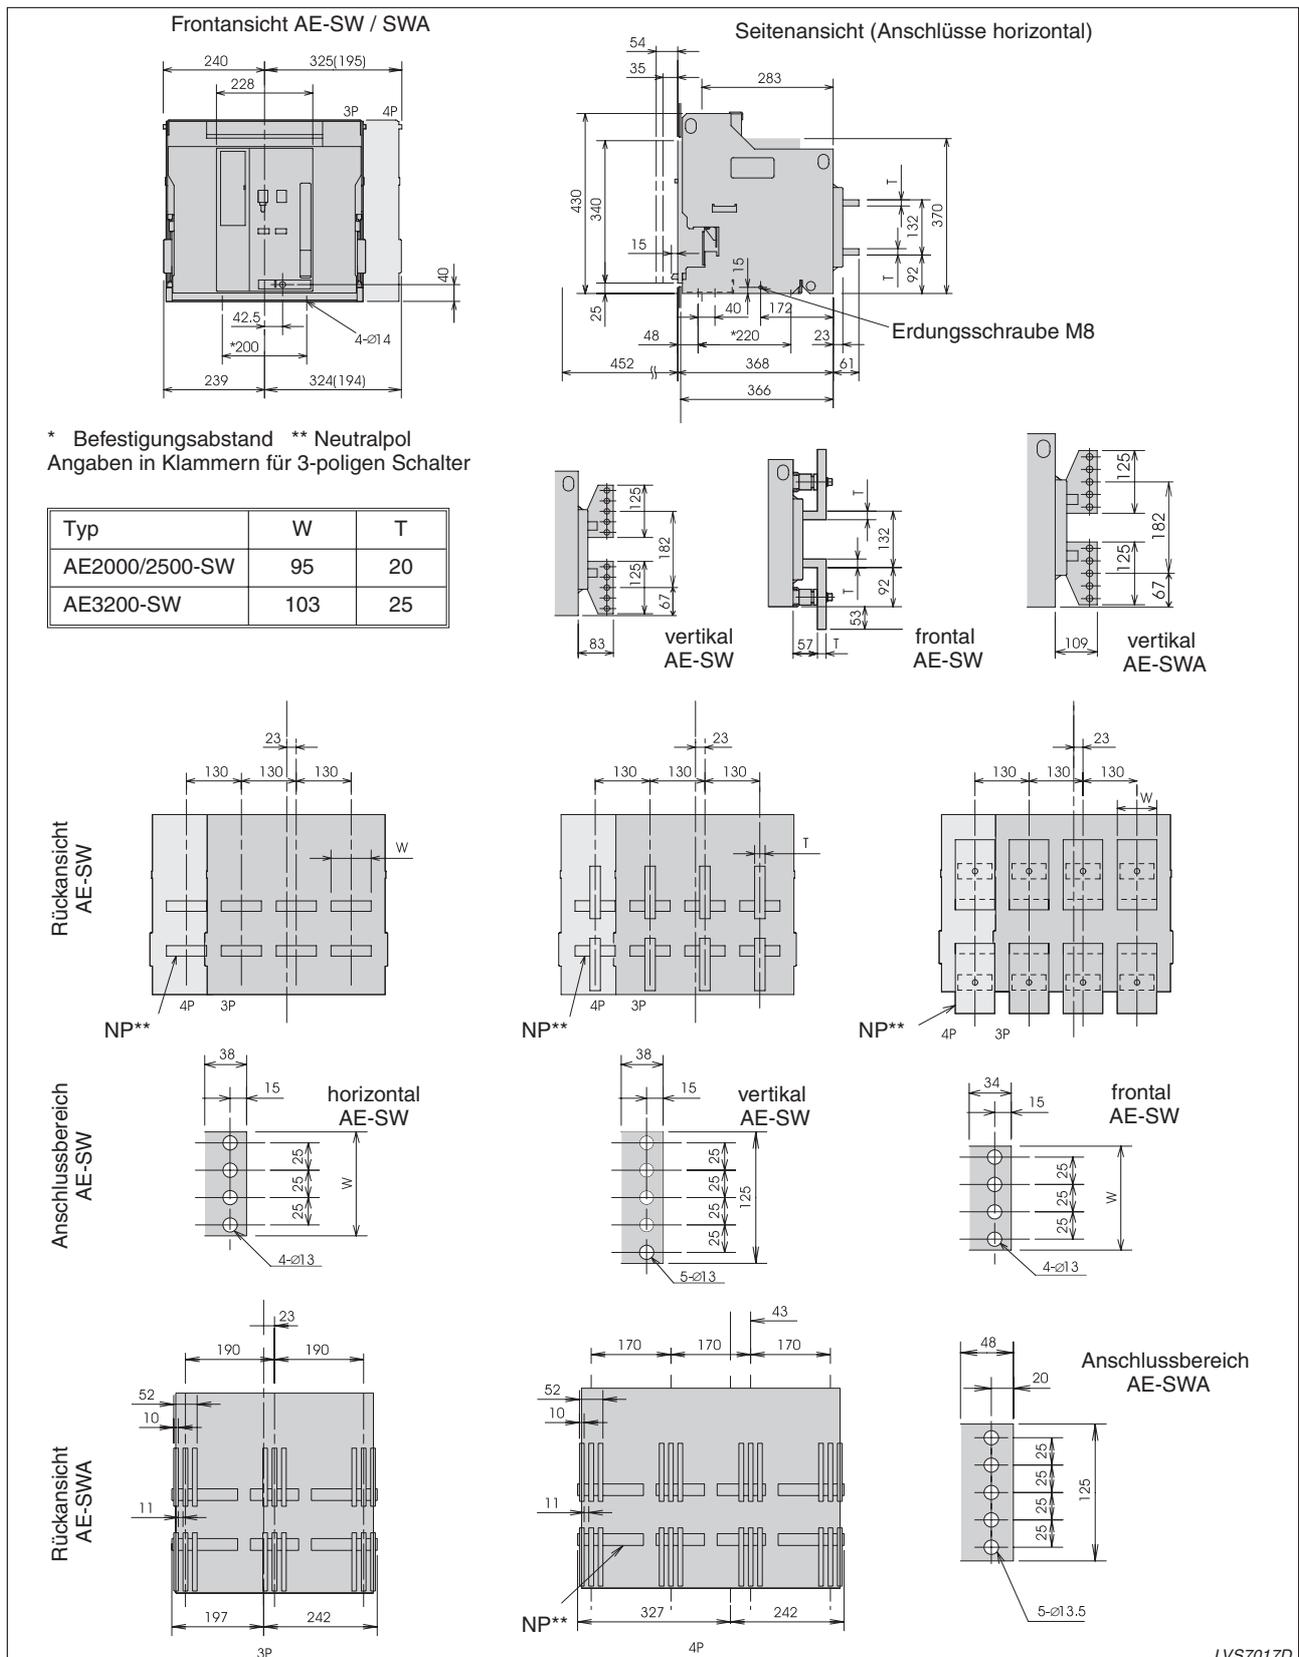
Abmessungen (in mm) der Schalter Einschubtyp
